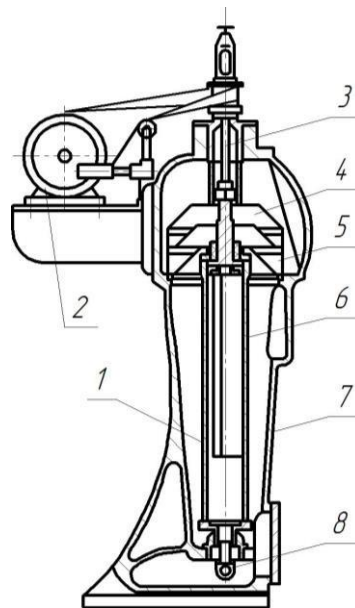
Схема зверхцентрифуги типу ОРТ: 1 – трьохлопадна крильчатка; 2 – електропривід; 3 – вал; 4 – верхня зливна тарілка; 5 – нижня зливна тарілка; 6 – трубчатий ротор; 7 – станина; 8 – сопло живлячого штуцера
